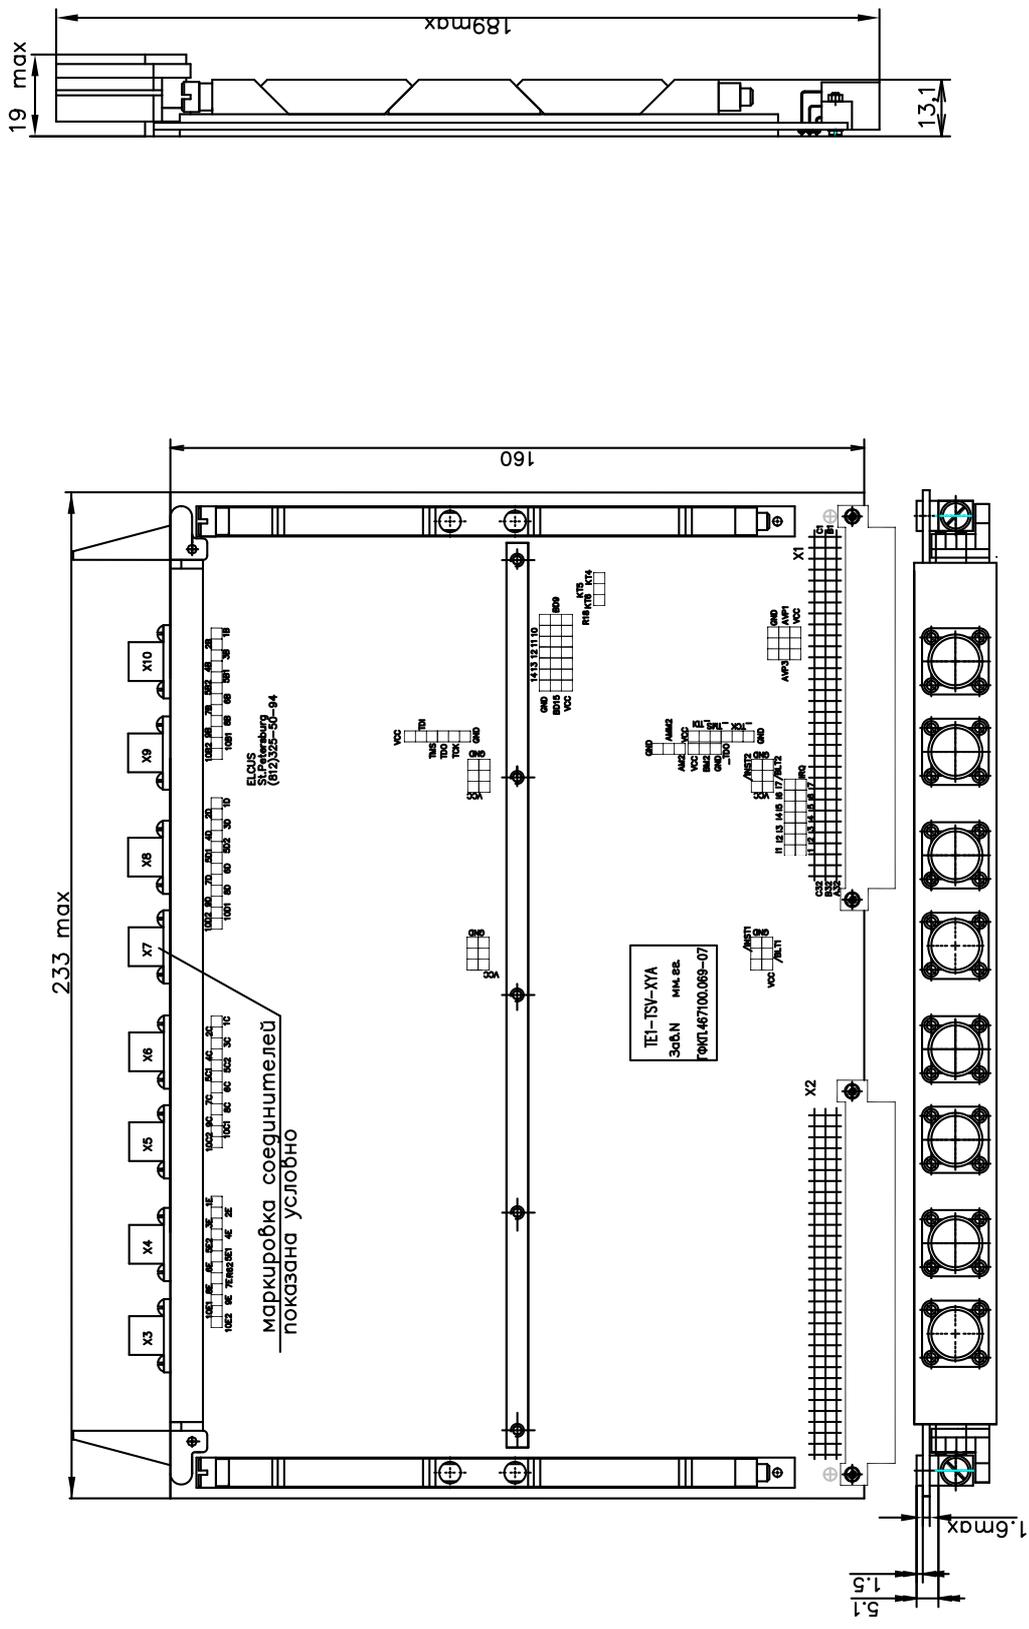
Габаритный чертеж модуля TE1-TSV-4R
